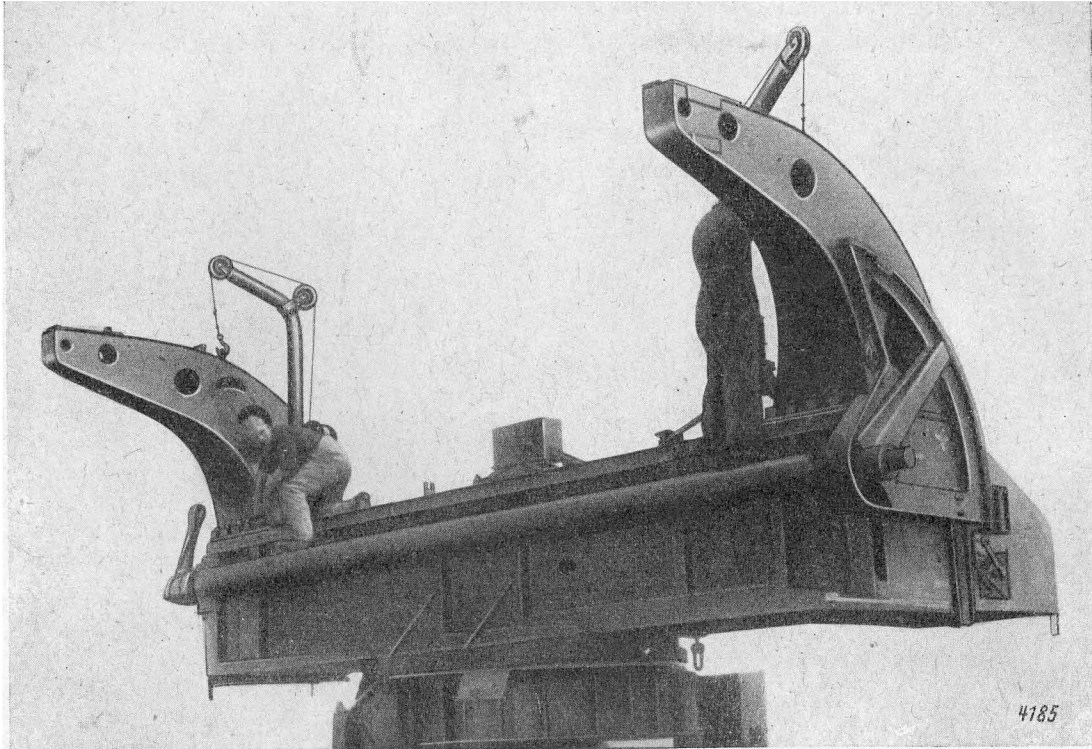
Tragarme auf den Hauptträger (III/3) niederlassen und die Befestigungsschrauben einführen. Mit Muttern leicht befestigen. Drahtseile lösen, Ausleger für die Schwenkkrane (IV/7) abnehmen und wegräumen, Paßbolzen einschlagen. Halteschrauben für die Tragarme anziehen.
